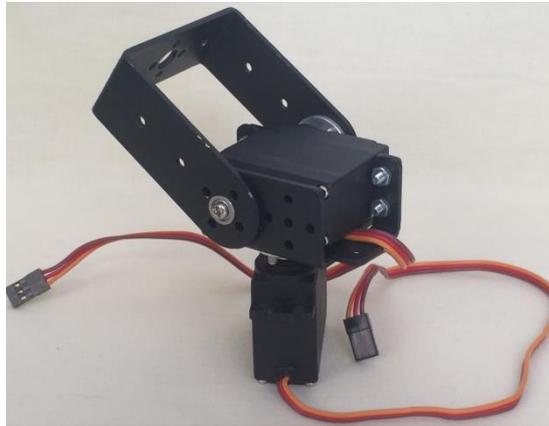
ENSAMBLE DE MECANISMO CABEZA
